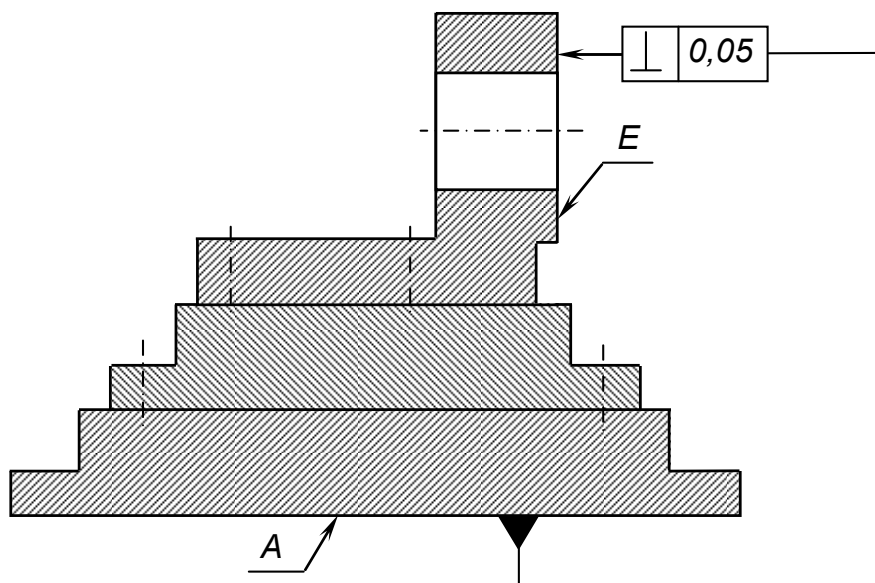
Конструктивна схема верстатного пристрою
